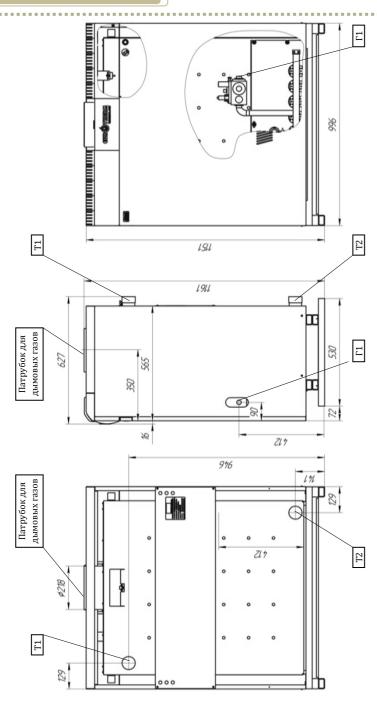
Установочный чертеж котла КТН 100 СЕ(Т)
